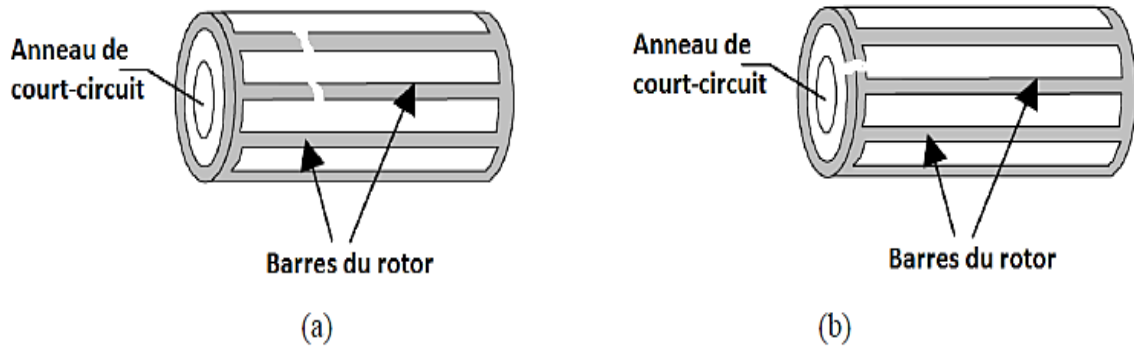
Défaut d'un rotor à cage d'écureuil :
